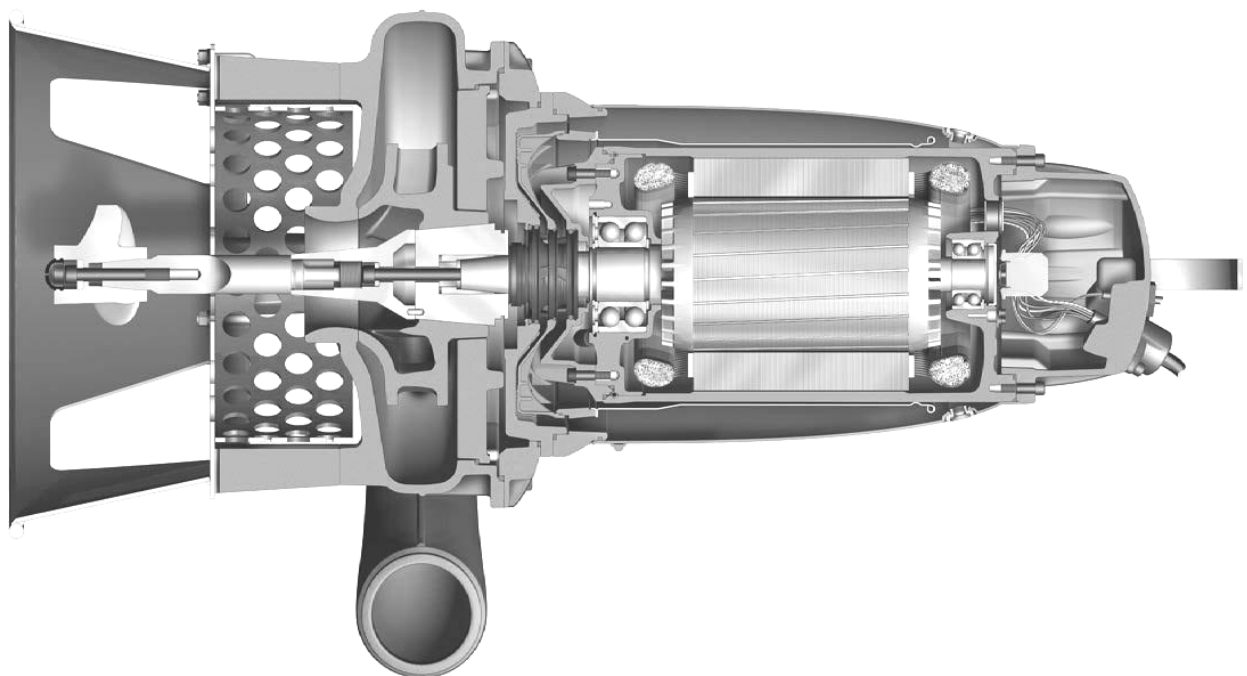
Бесштанговый погружной (герметический) центробежный насос в разрезе
